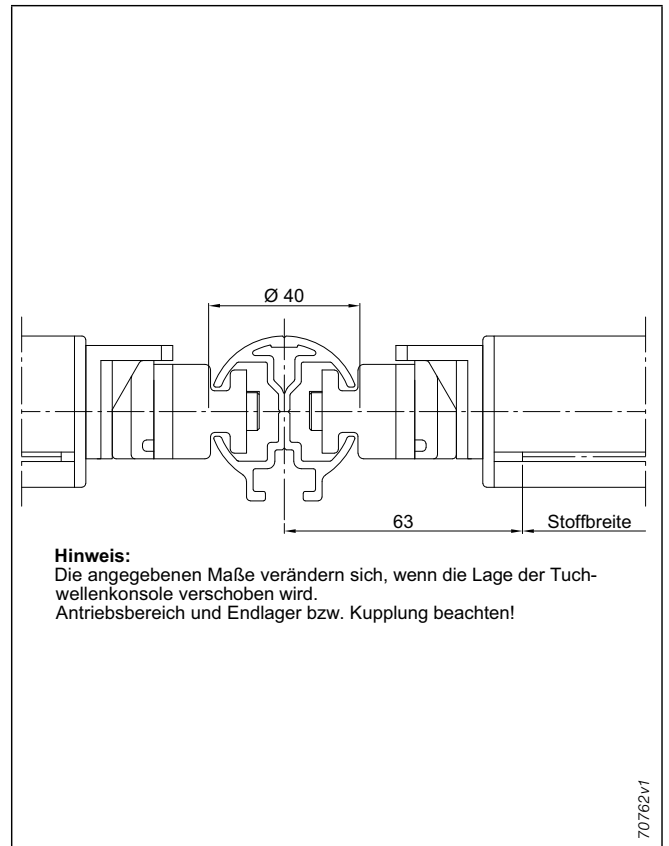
Details Führungsschiene Ø40 mm – Stoffabzugsmaße für Typ 101
